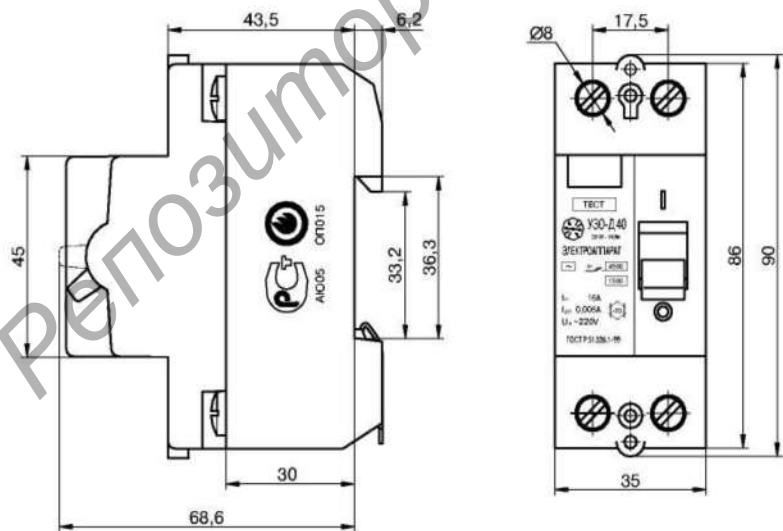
Общий вид и габаритные размеры двухполюсного УЗО типа Д-40 для монтажа на DIN-линейку шириной 35 мм
